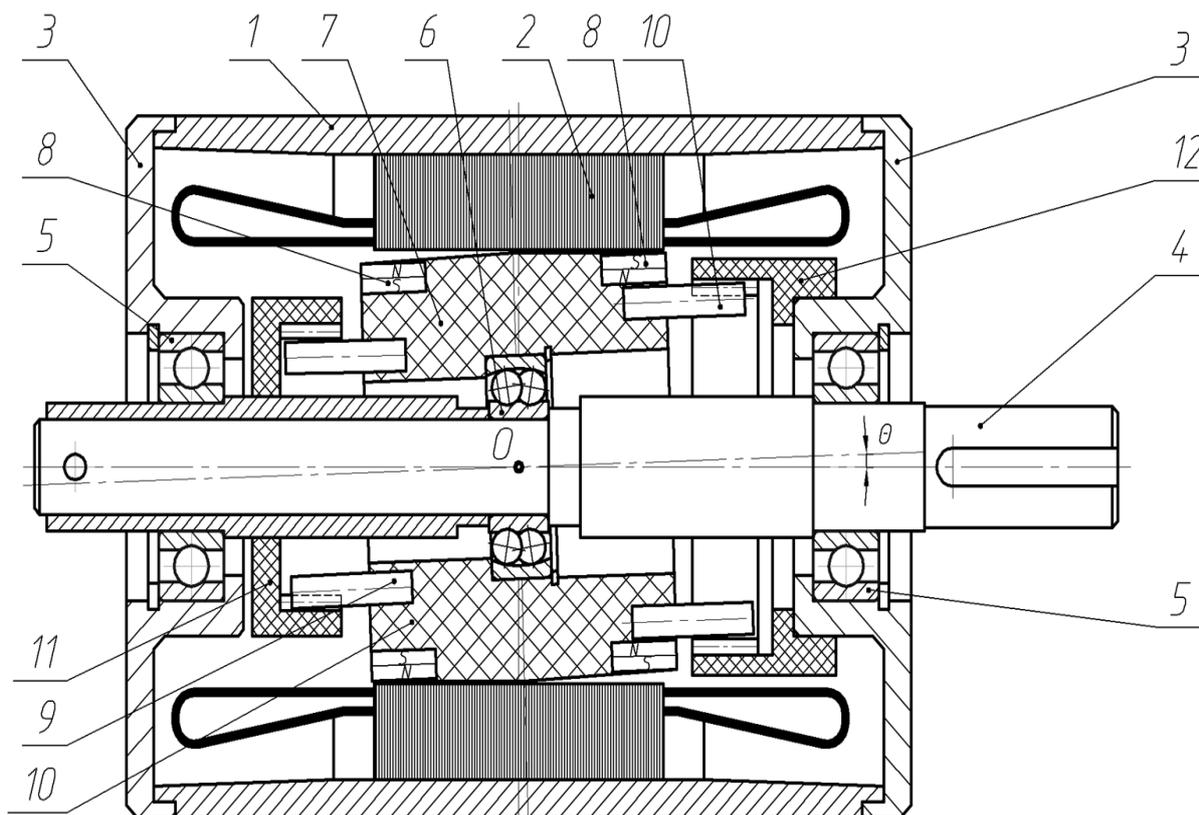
Общий вид конструкции магнитного привода с зубчатым зацеплением прецессионного типа
